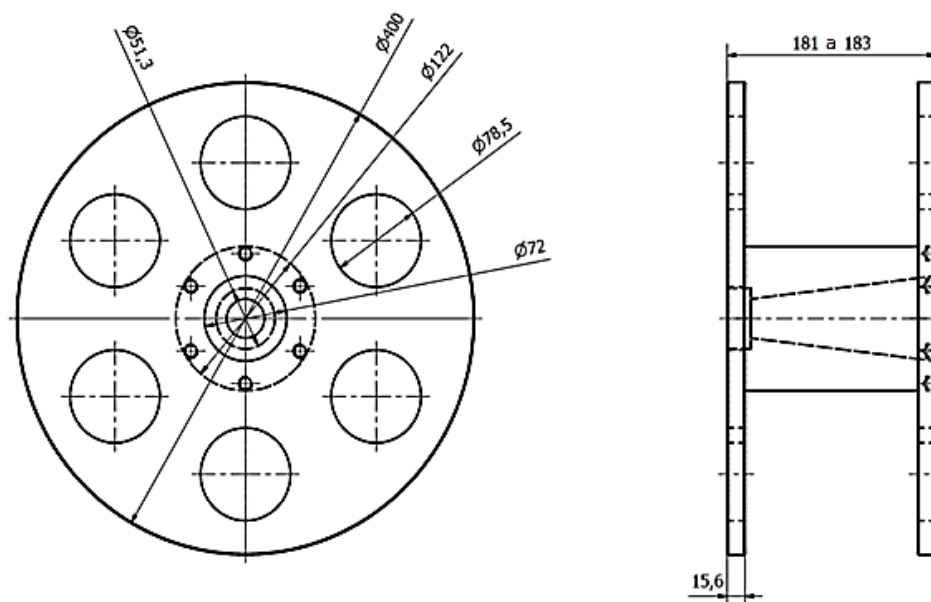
Dimensões teóricas de uma bobina inserida nas máquinas eletronicamente modificadas – abas espessas.
